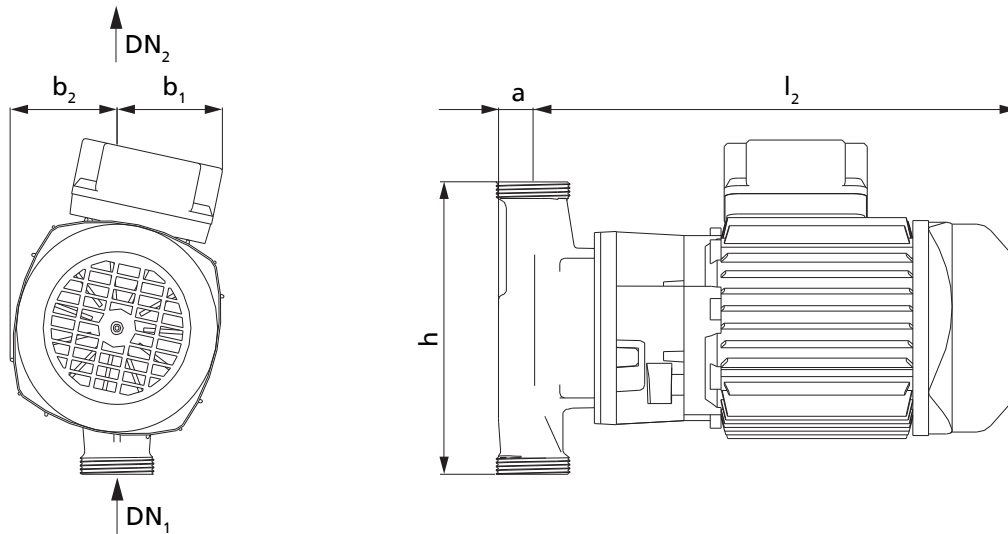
Abmessungen Pumpenaggregat mit Gewindeanschluss, Baugröße < 032-032-100
